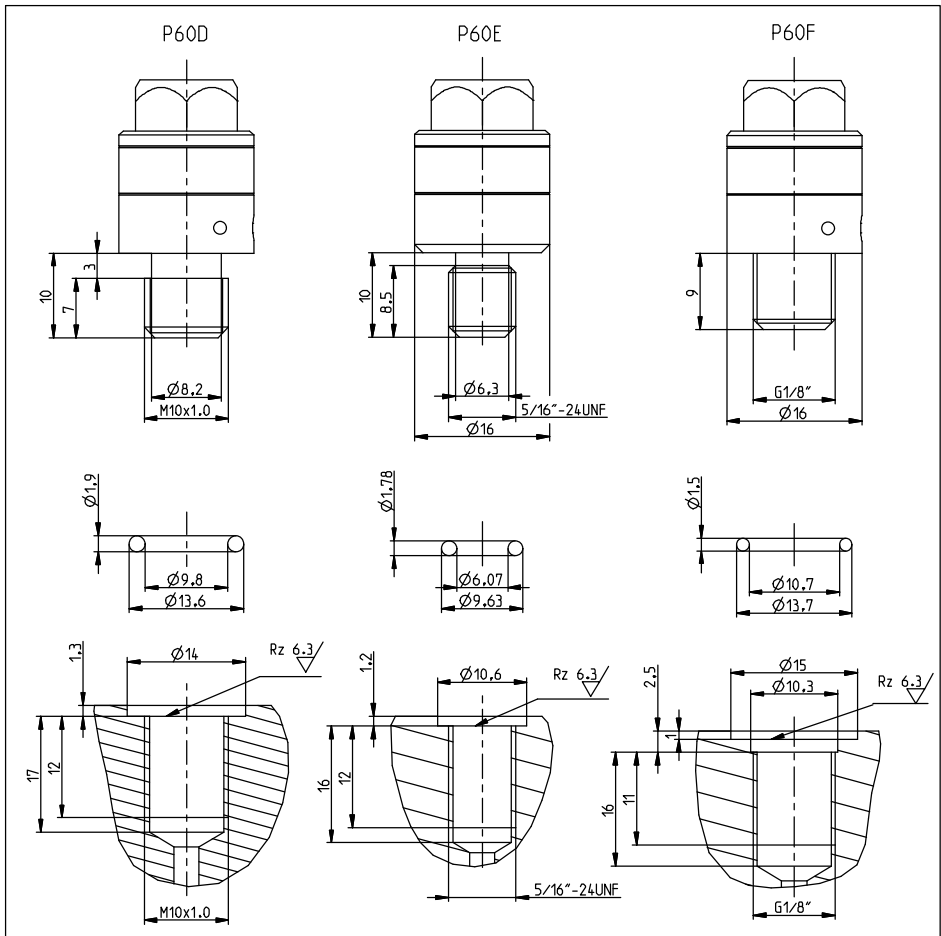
Geometrie der Anschlussstelle der Druckaufnehmer P60D, P60E und P60F
